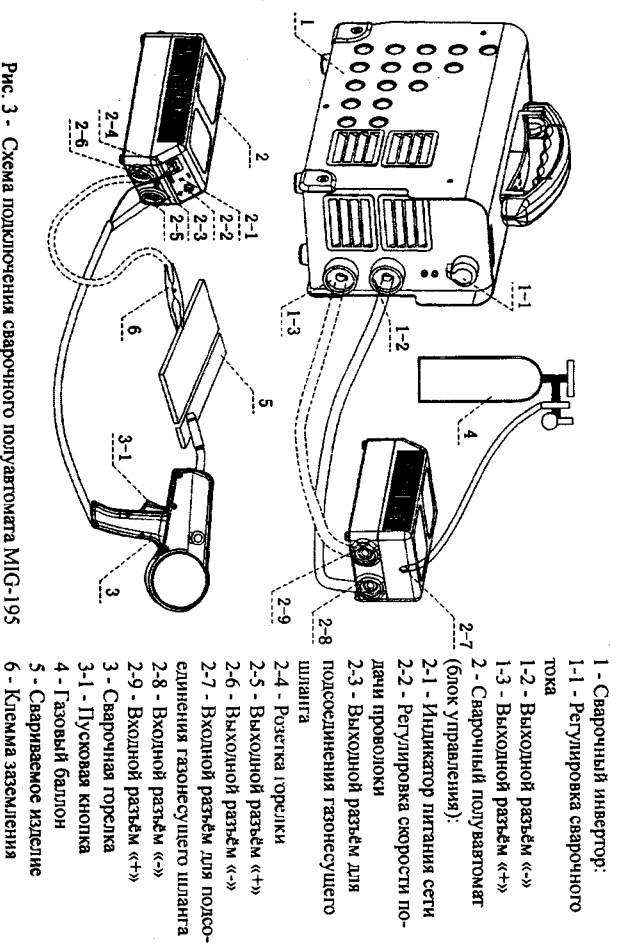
Схема подключения сварочного полуавтомата MIG-195
